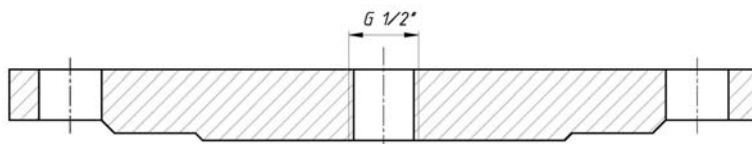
Крышка фланца с резьбой G 1/2".
